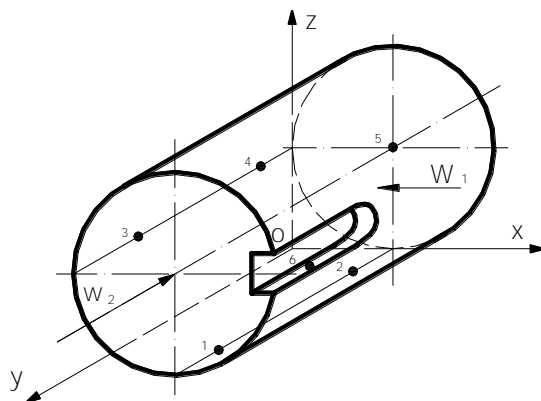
Схема установки длинной цилиндрической детали.
